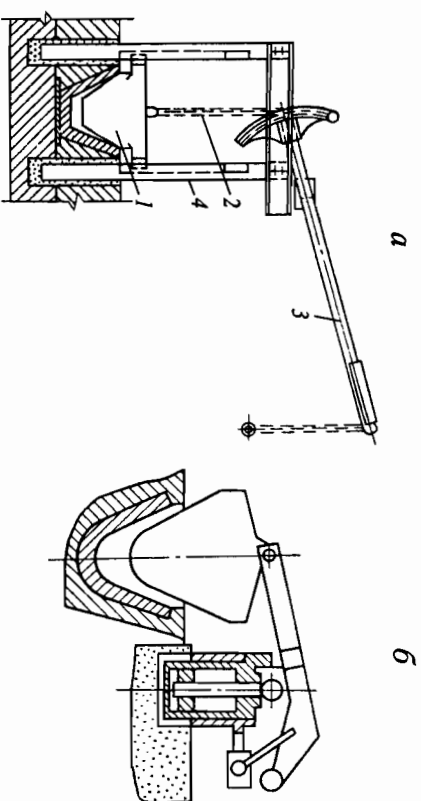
Отсечное устройство для чугуна и шлака (а) и с центральным пневматическим приводом (б)
